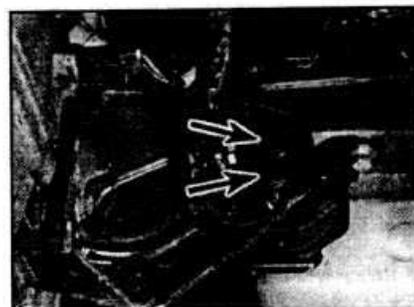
А.23. Расположение болтов крепления левой передней подвески силового агрегата.
